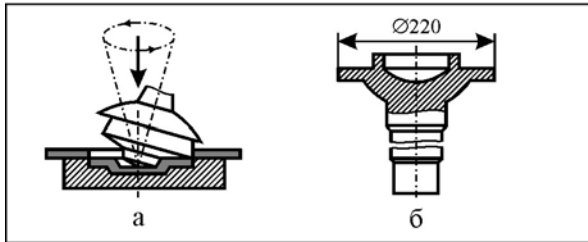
Схема сферорушійного штампування низької деталі великого діаметру (а) та приклад обробленої даним способом довгої деталі (б)
